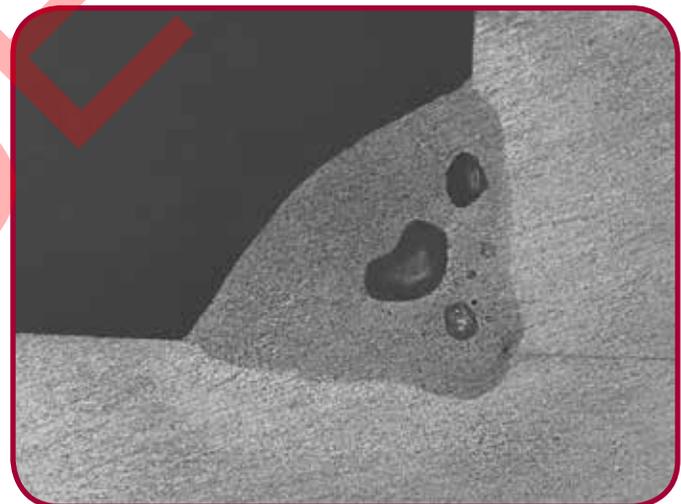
Ataque químico macroscópico en una soldadura de filete mostrando porosidad de gran tamaño y forma irregular.
